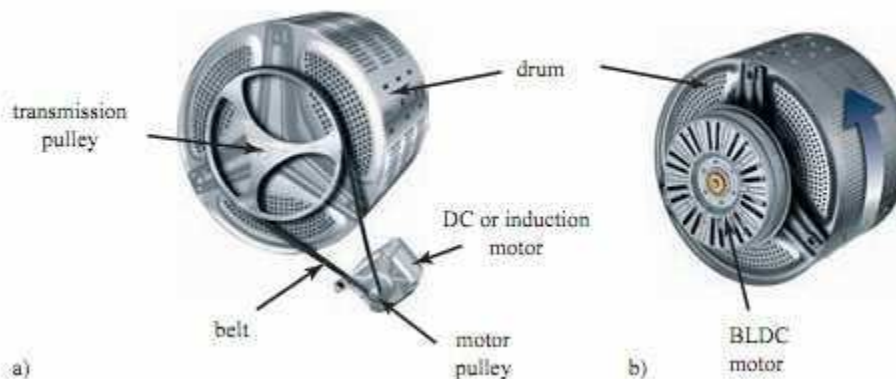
a) machine à laver classique b) machine à laver a entraînement directe [27]
